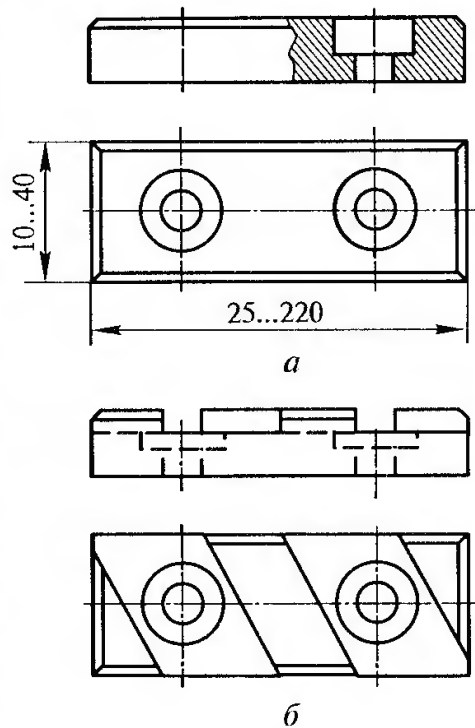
Опорні пластини для установки заготовок на оброблені поверхні
